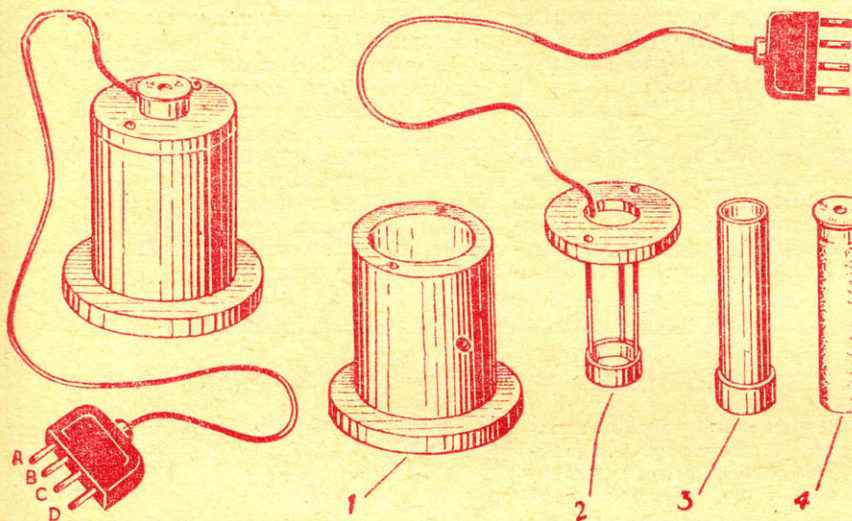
Конструкция датчика: 1 — корпус; 2 — крышка; 3 — внутренний опорный стакан; 4 — двигатель.
